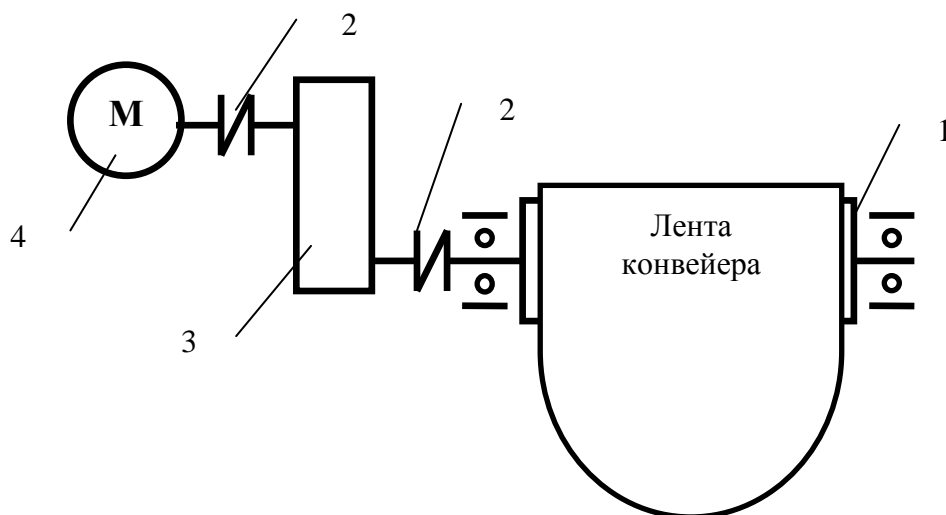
Кинематическая схема привода ленточного конвейера
